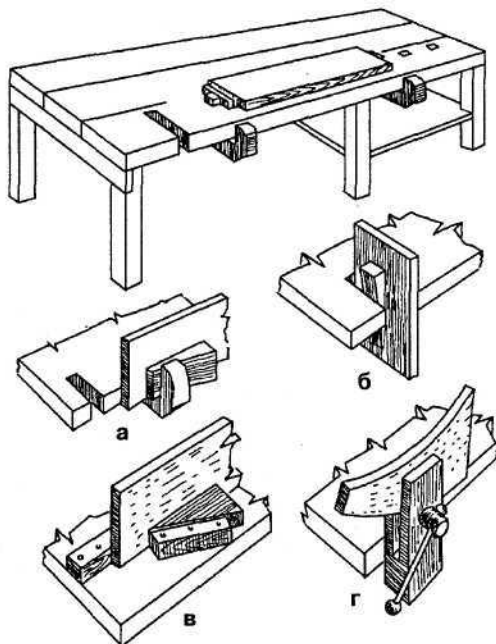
Верстак и зажимные приспособления: а, в — клиновые зажимы для обработки кромки доски; б — зажим для обработки торцов доски; г — столярные тиски
